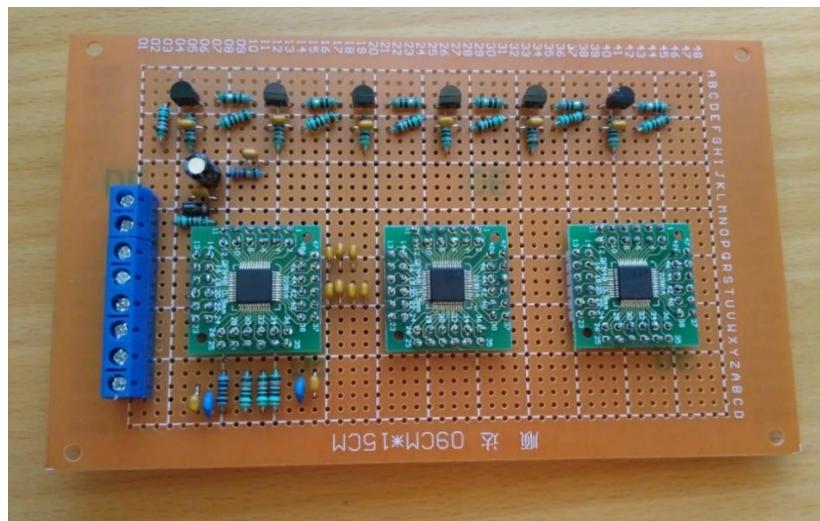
Todos los elementos electrónicos auxiliares, zona de balanceo pasivo (parte superior de la PCB) y Daisy Chain del primer microchip soldados
